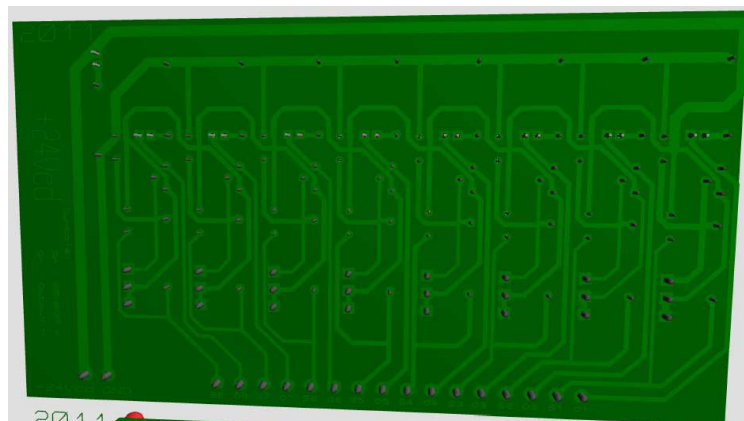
Vaqueta impresa con el diseño del circuito electrónico
